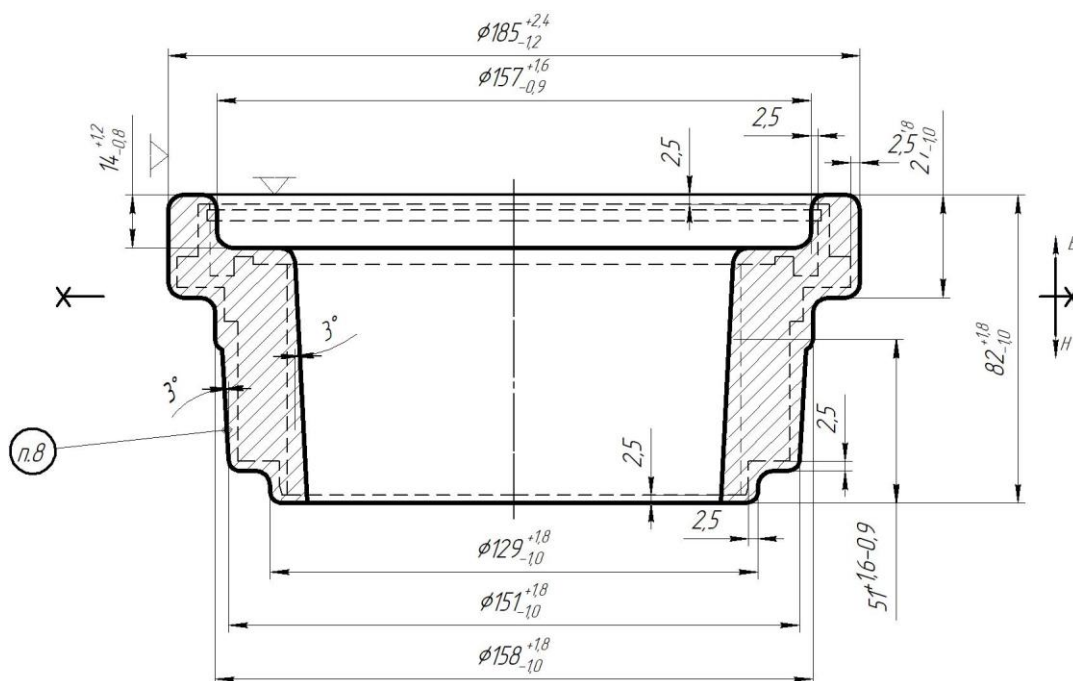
Ескіз заготовки виконаної на КГШП.
